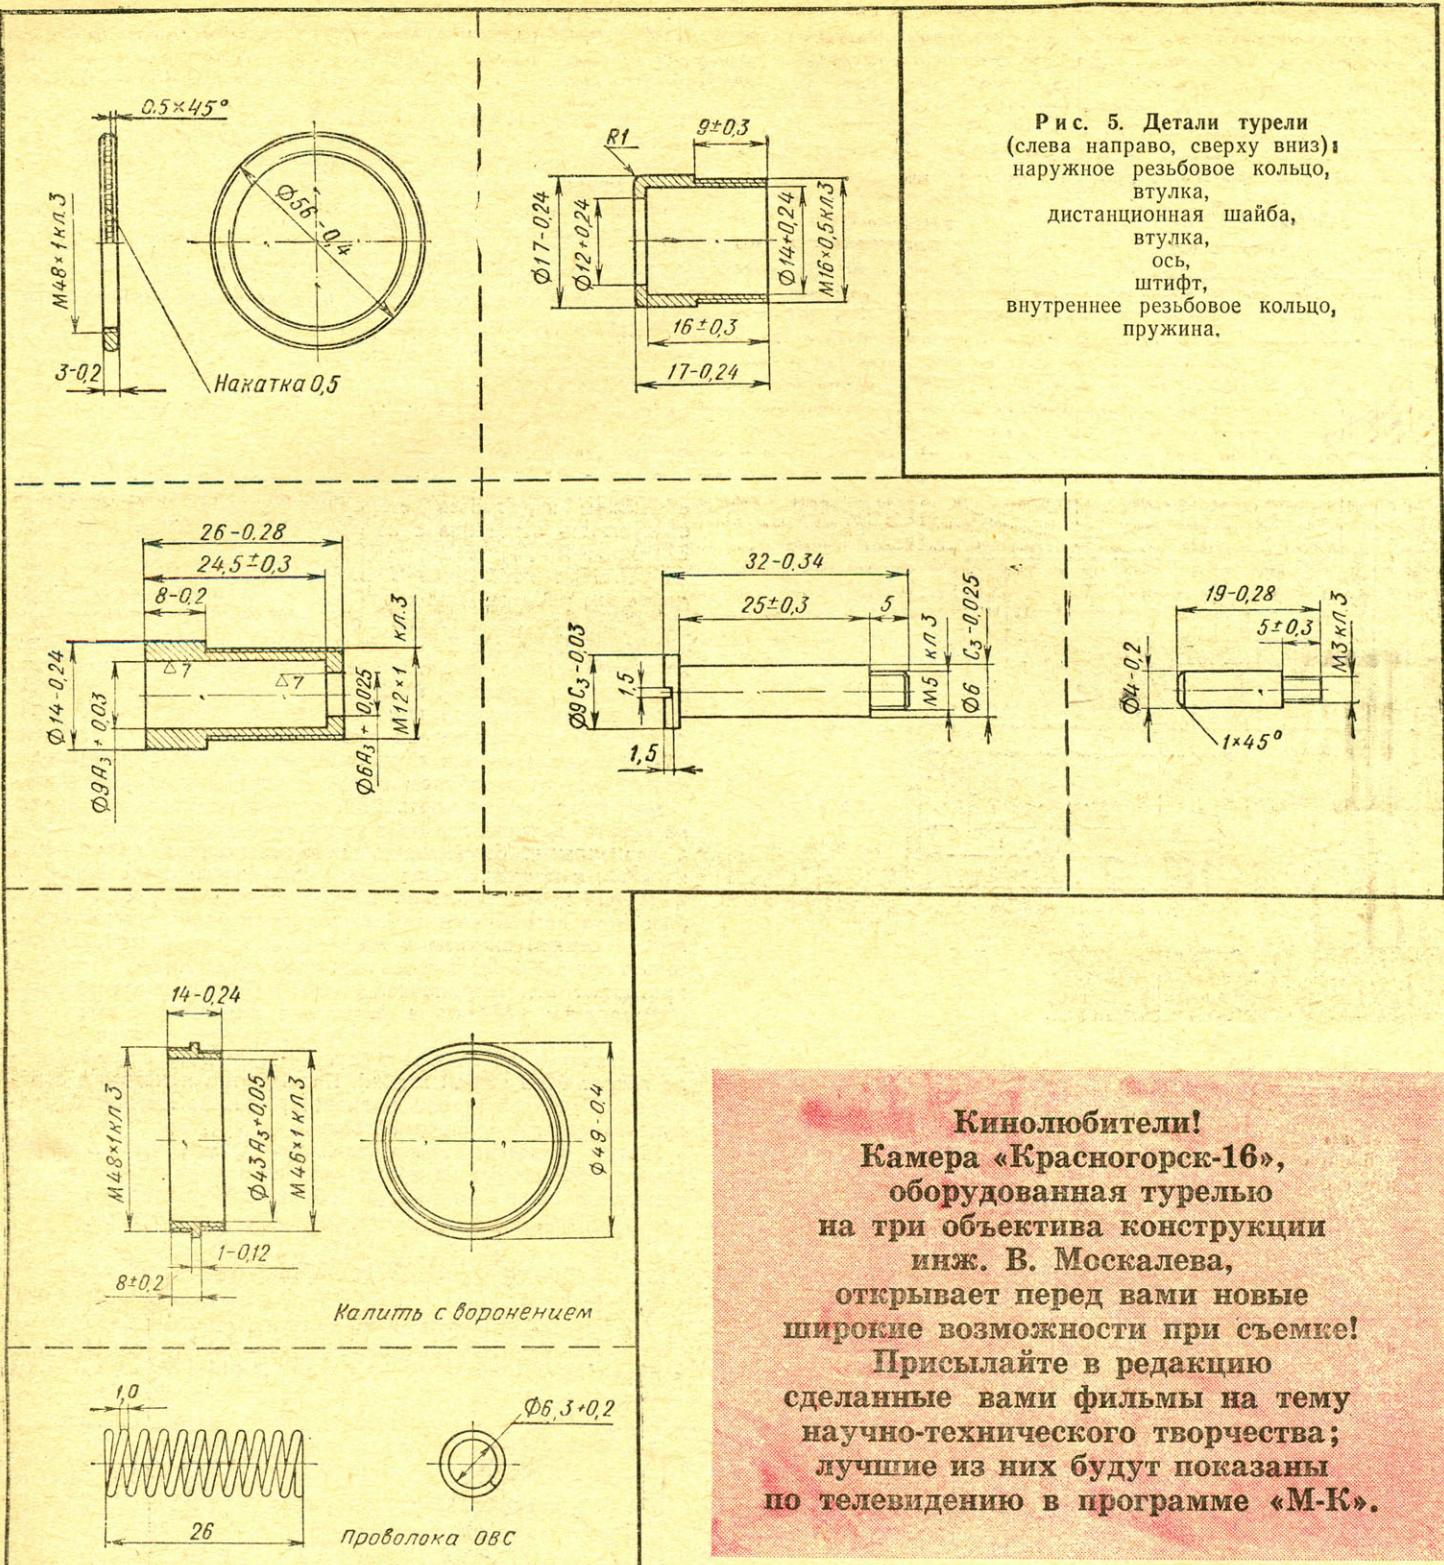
Детали турели (слева направо, сверху вниз): наружное резьбовое кольцо, втулка, дистанционная шайба, втулка, ось, штифт, внутреннее резьбовое кольцо, пружина.
